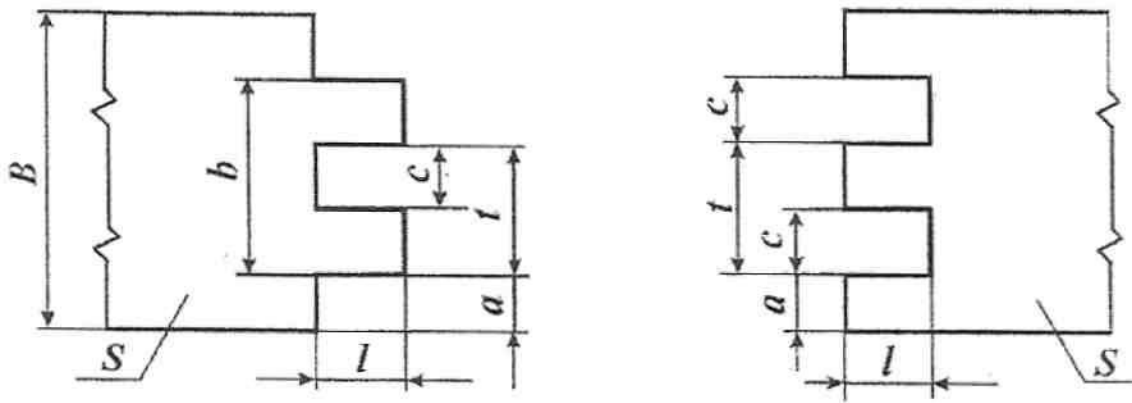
Схеми деталей з'єднання на шип подвійний відкритий
